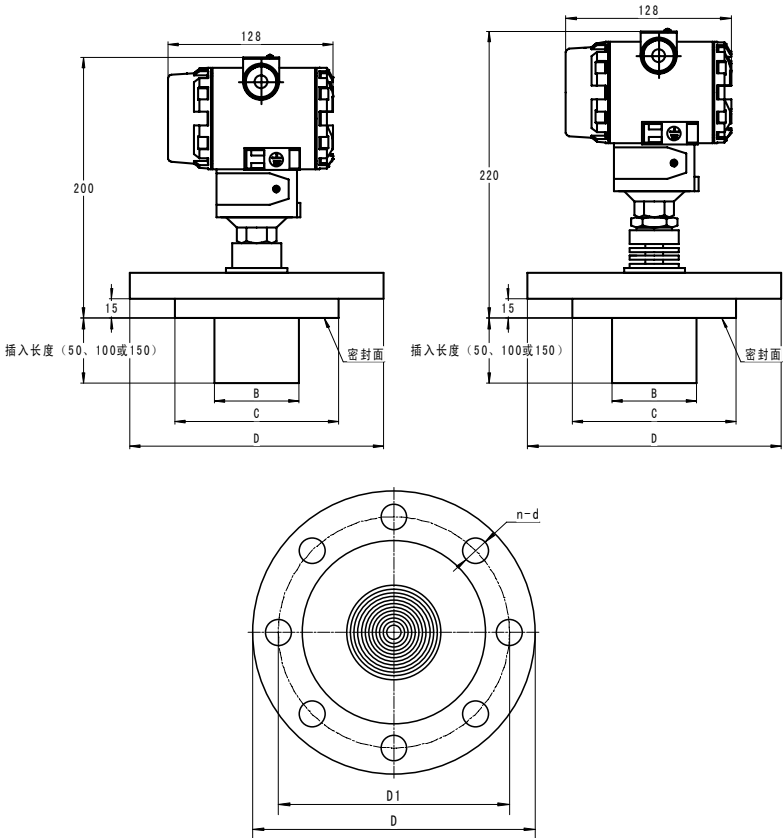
FB3351T 型智能压力变送器外形尺寸图
